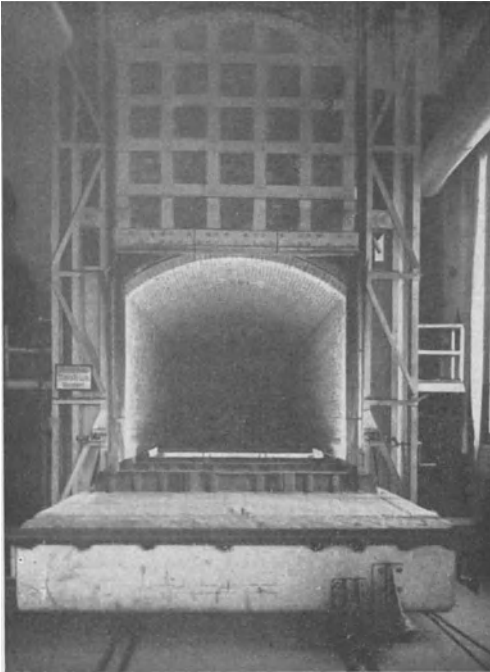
Großraum-Glühofen für schwere Schweißkörper.
